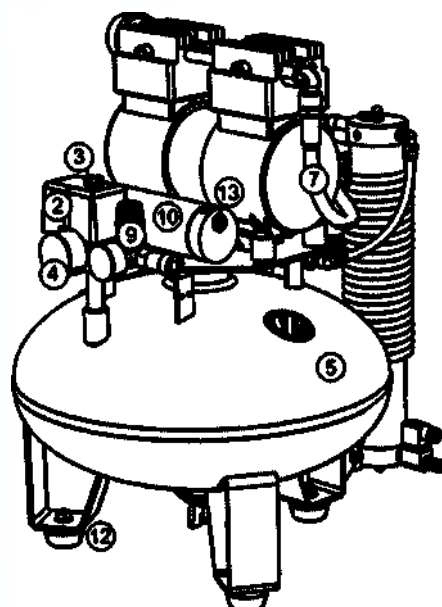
Общий вид компрессора KM-24.OLD10Д
